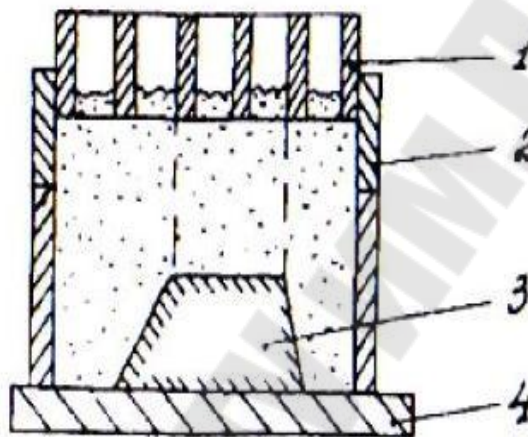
Схема прессования решетчатой прессовой плитой: 1 – решетчатый элемент; 2 – наполнительная рамка; 3 – модель; 4 – модельная плита
